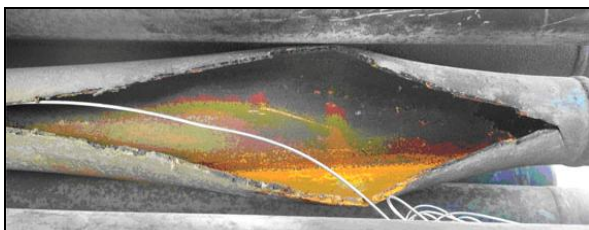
Вид аварийной трубы  $\varnothing 50 \times 3$  мм внутри котла-утилизатора / Fig. 1. Type of emergency tube  $\varnothing 50 \times 3$  mm inside the recovery boiler
